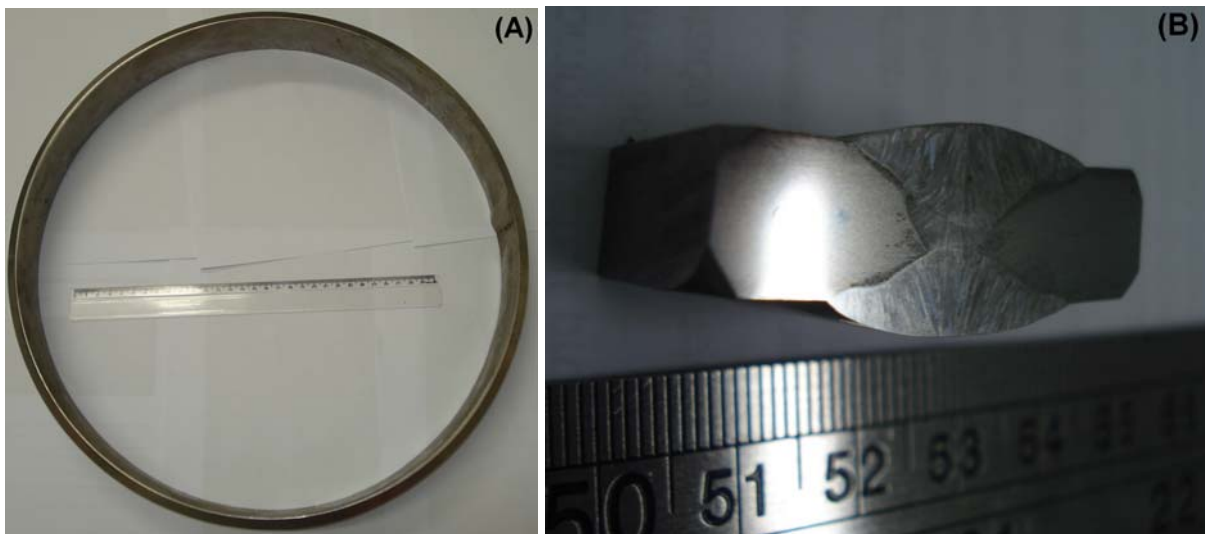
Amostras analisadas: (a) tubo; e (b) junta soldada.
